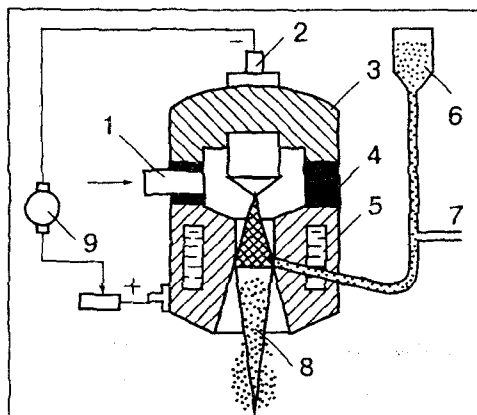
Схема плазменного напыления порошком: 1 — подвод плазмообразующего газа; 2 — катод плазмотрона; 3 — корпус катода; 4 — изолятор; 5 — корпус анода; 6 — порошковый питатель; 7 — подвод газа, транспортирующего порошок; 8 — плазменная дуга; 9 — источник питания
